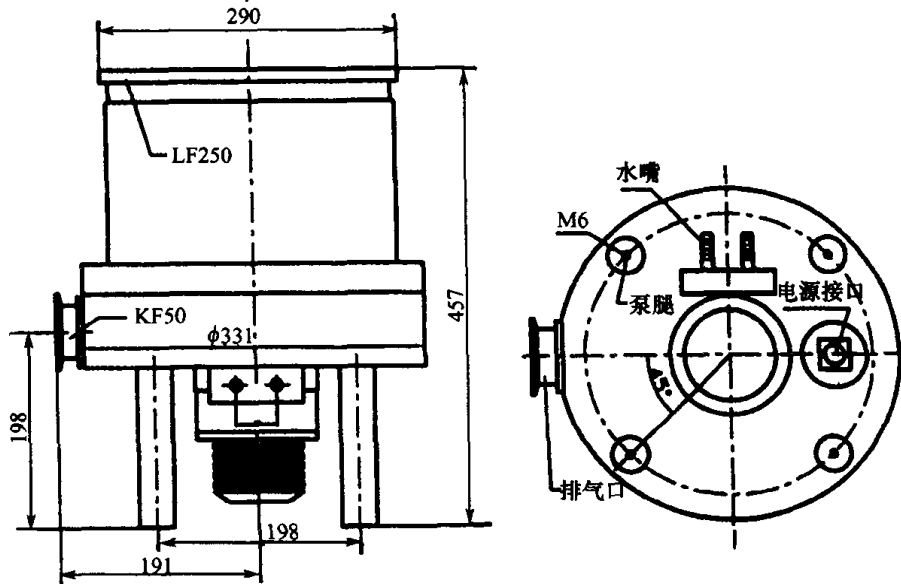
F-250/1500 涡轮分子泵安装尺寸
